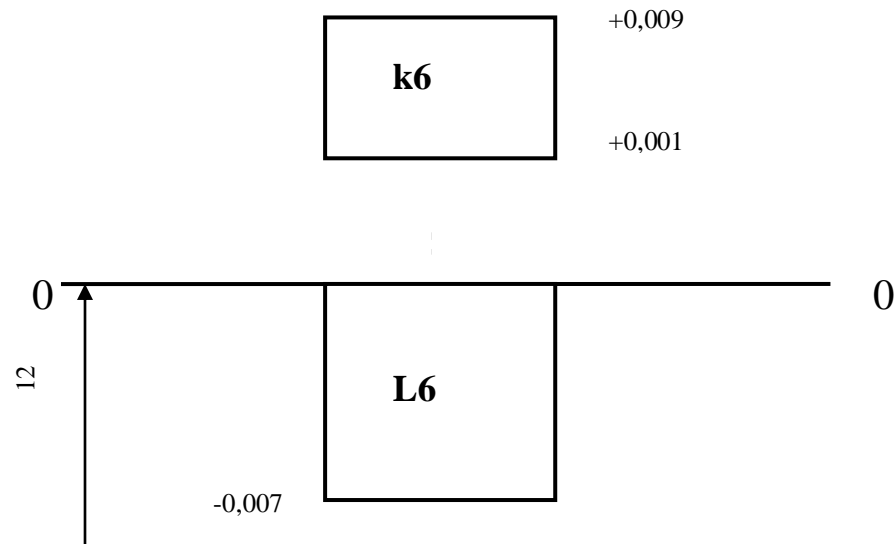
Схема посадки внутреннего кольца подшипника на вал
